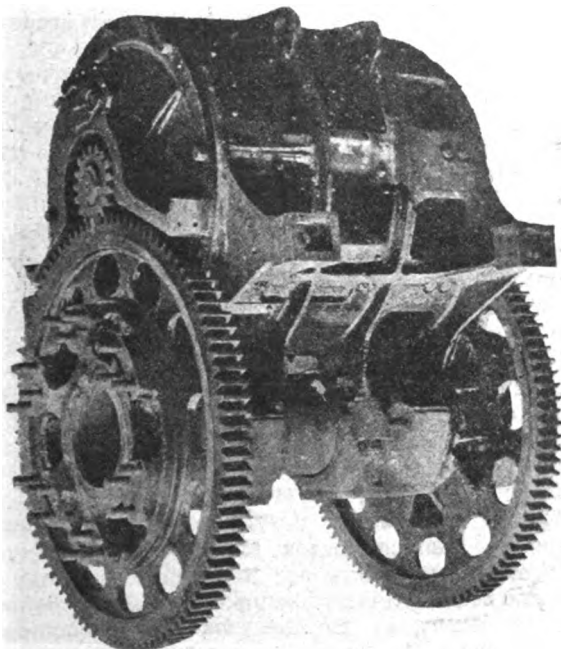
Motore ed asse cavo con ingranaggi delle locomotive della New Haven.
